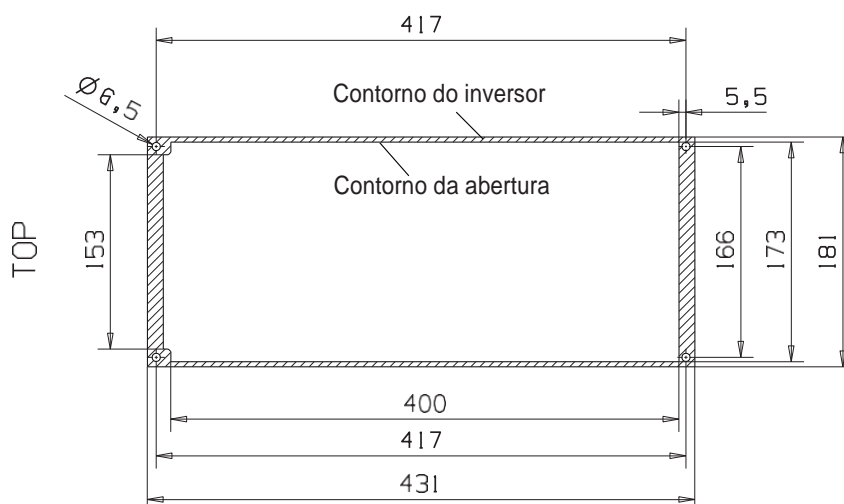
Dimensões do recorte para montagem com flange do MR4 ao MR6 (unidade: mm)
